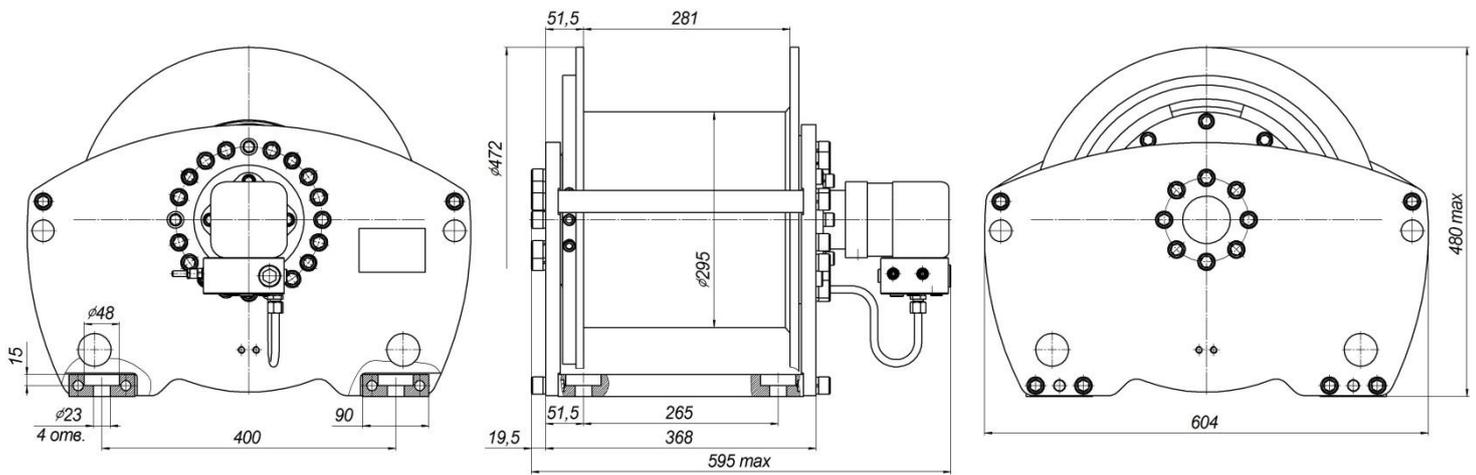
Общий вид, габаритные и присоединительные размеры
